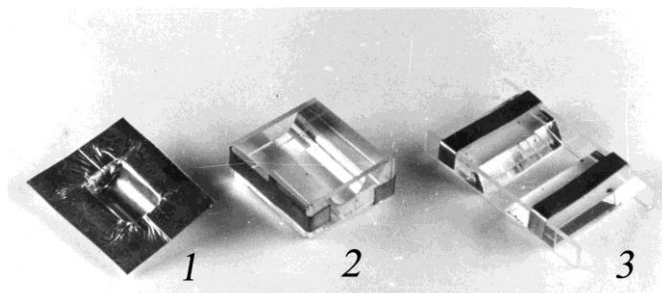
Первые опытные матрицы для изготовления элементов из термопластичного стекла: 1 – полужидкий цилиндр (одноразовая матрица из Al-фольги), 2 – полужидкий цилиндр (разъемная матрица из полированного стекла), 3-матрица для изготовления элементов МНПВО с разным числом отражений (разъемная матрица из полированного стекла). Изготовлены в мастерских «ГОИ им. С. И. Вавилова».
